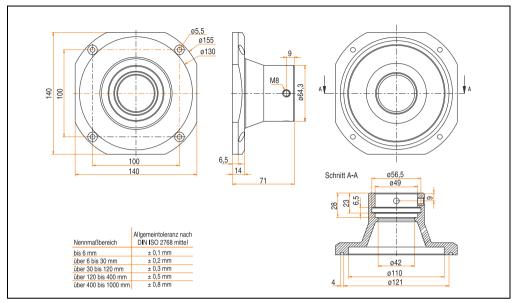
Abmessungen Extension Flansch 5AC800.FLG1-00
